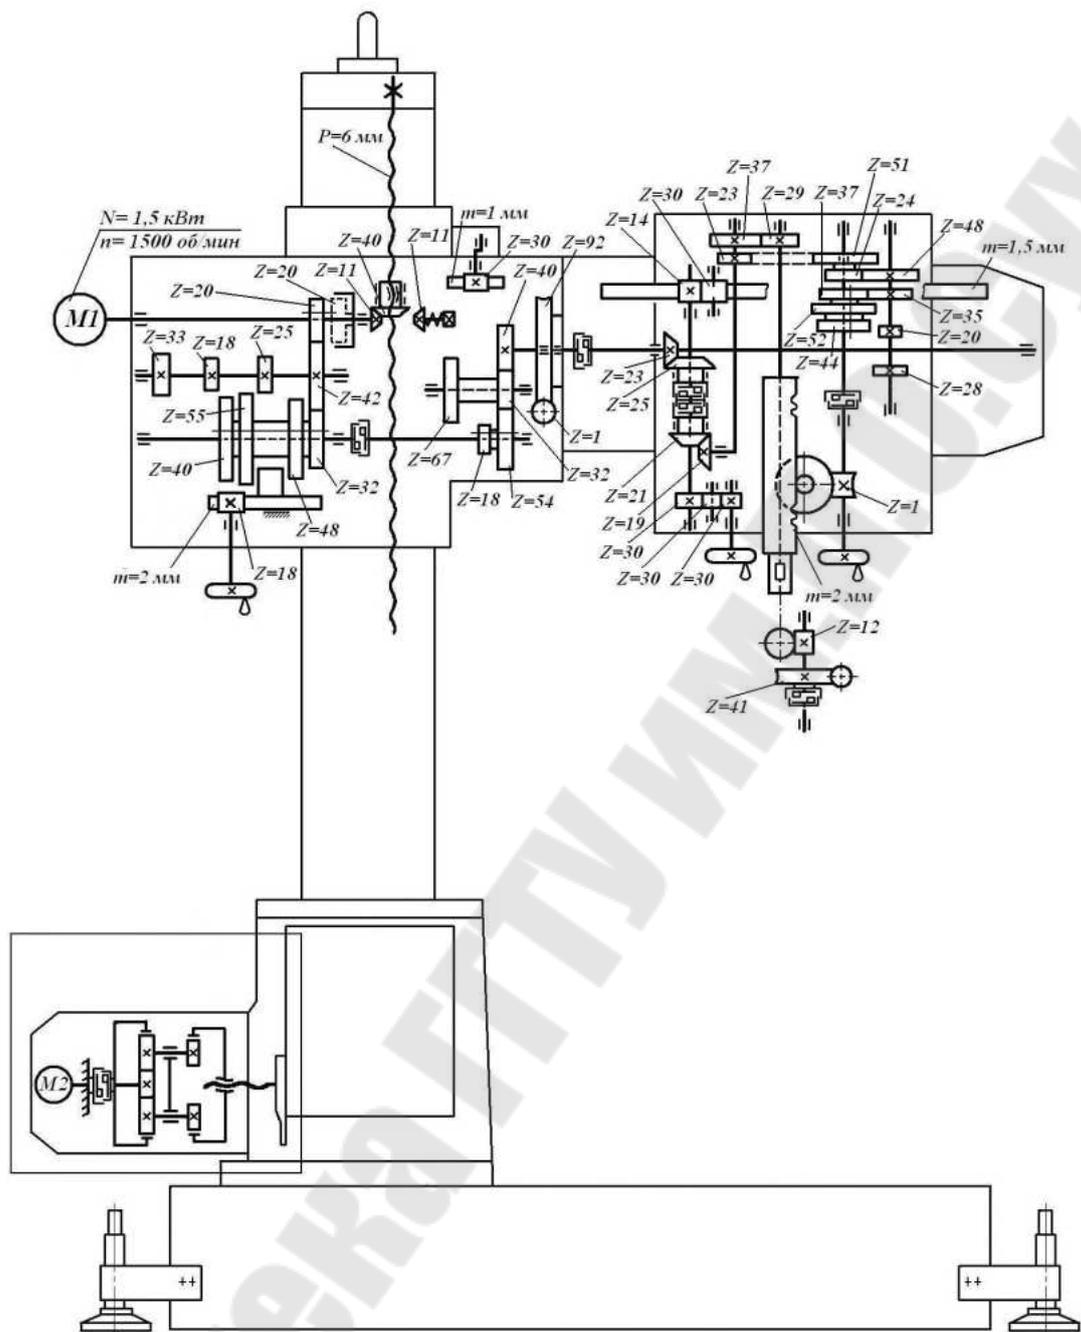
Кинематическая схема радиально-сверлильного станка 2К52-1
